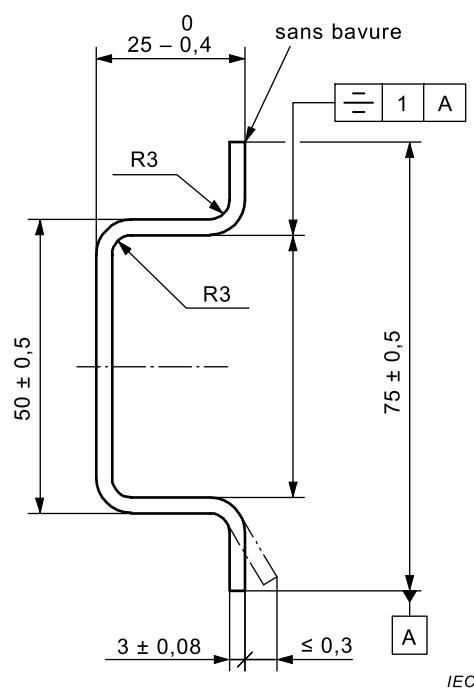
Profilé à section en forme de chapeau de largeur 75 mm pour fixation d'équipements par encliquetage
